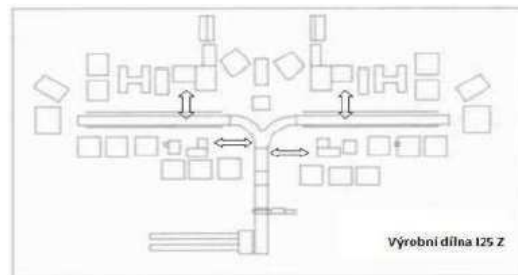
Obecná ilustrácia layoutu výrobní haly (Topkins et al., 2010)
